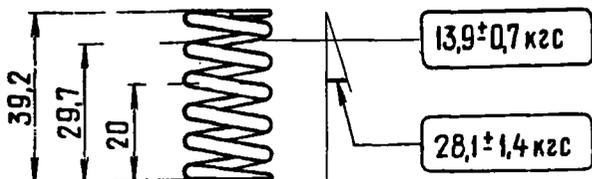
Основные данные для проверки внутренней пружины клапана
